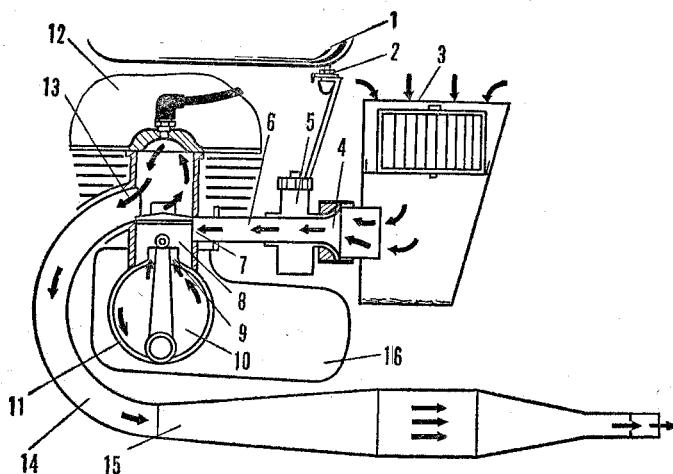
Схема порядка работ по форсировке двухтактного двигателя: 1 — бензиновый бак; 2 — бензокраник; 3 — воздушный фильтр; 4 — насадка карбюратора; 5 — карбюратор; 6 — впускной патрубок; 7 — впускной канал; 8 — поршень; 9 — перепускной (продувочный) канал; 10 — коленчатый вал; 11 — кривошипная камера; 12 — головка цилиндра; 13 — выпускной канал; 14 — выпускная труба; 15 — глушитель; 16 — коробка передач
